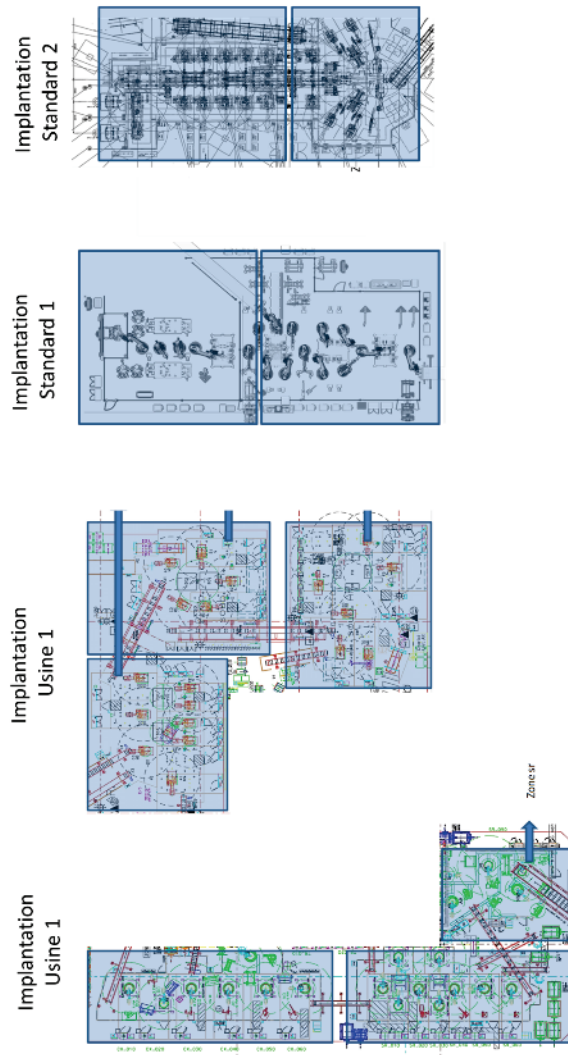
Architectures d'implantation d'assemblage de plancher arrière
